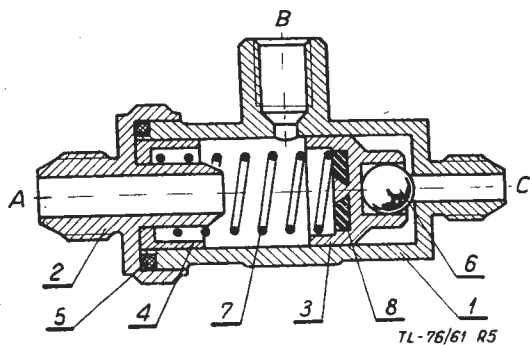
Zawór zwrotny hydrauliczny. 1 — korpus; 2 — łącznik; 3 — kulka; 4 — sprężyna; 5 — uszczelka; 6 — drut zabezpieczający
